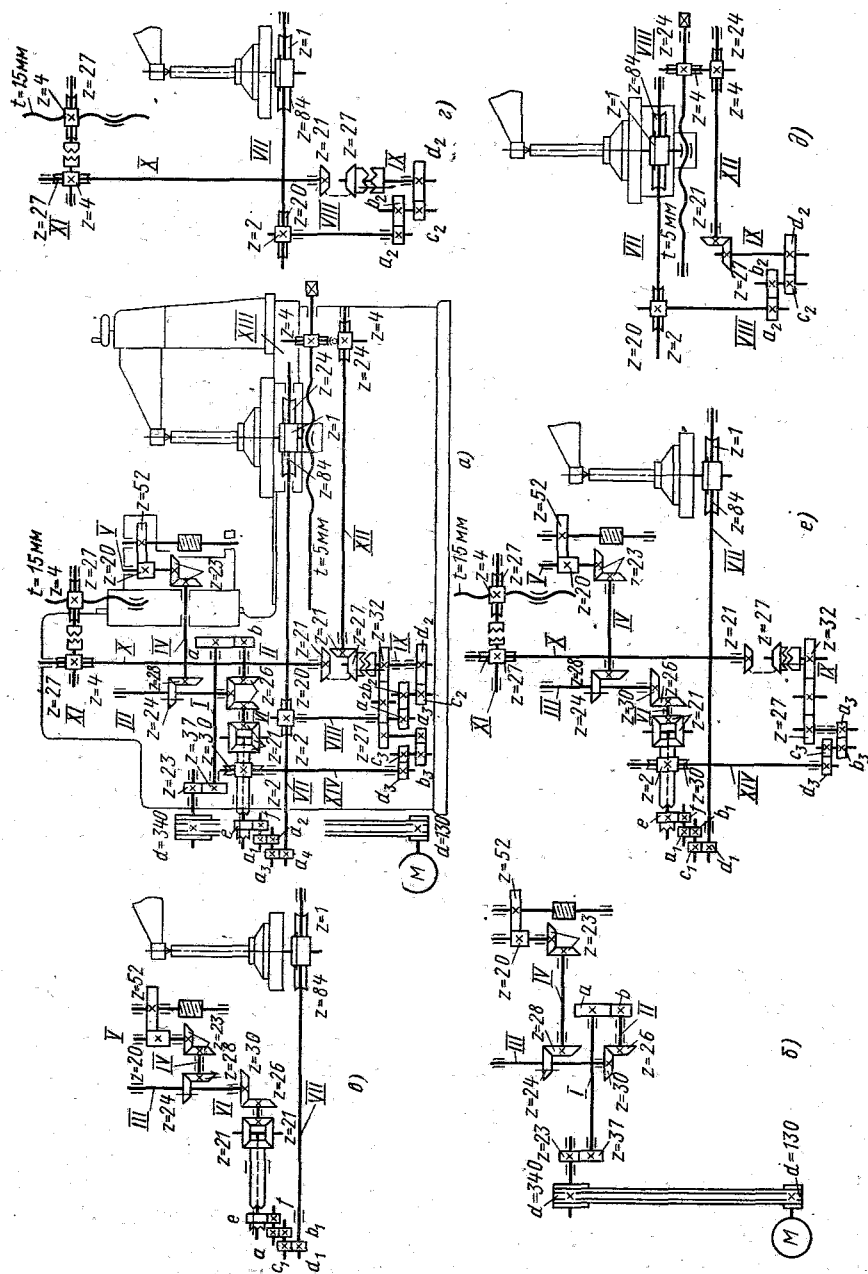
Кинематическая схема зубофрезерного станка мод. 532
